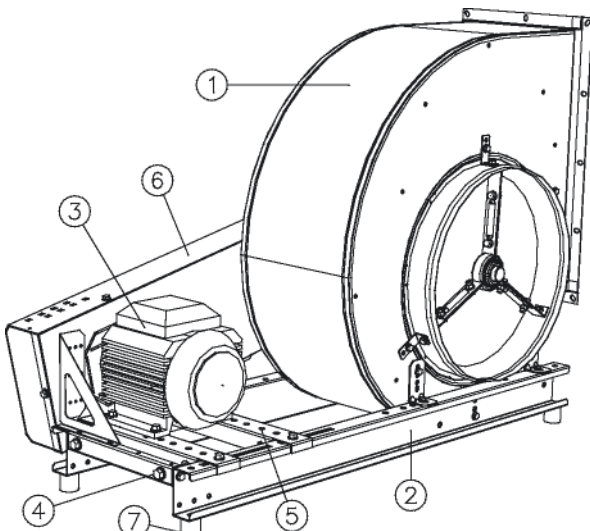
Elementos del ventilador GT-3 (dimensiones 025...071).
